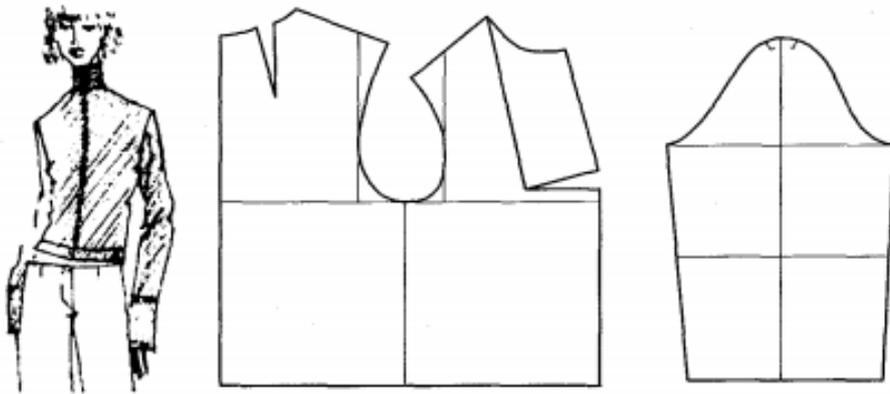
Схема конструкции изделия с втачными рукавами
